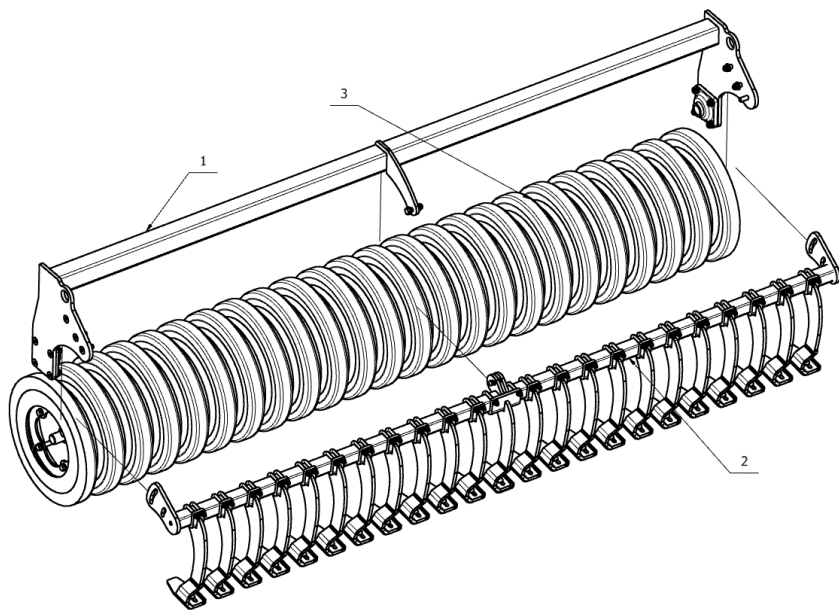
Wał crosskill Ø380mm – mocowanie skrobaka.
